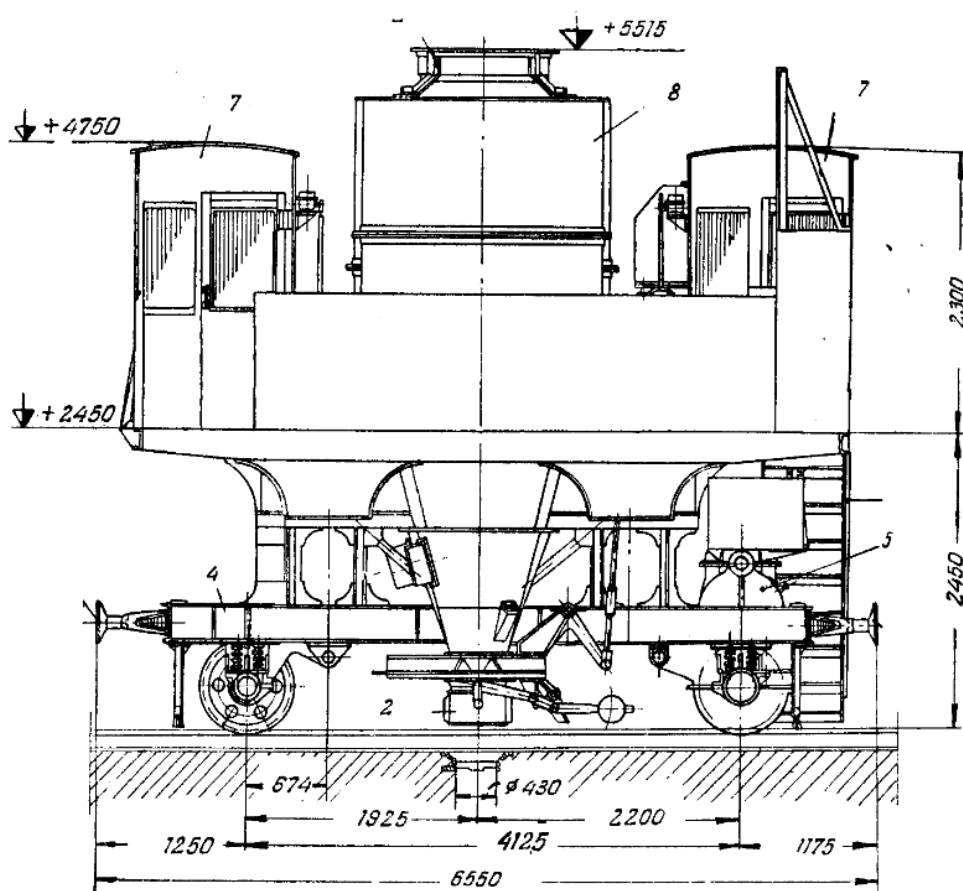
Трьохбункерний вуглезавантажувальний вагон конструкції конструкторського бюро Главмашмета. Вид зліва.
